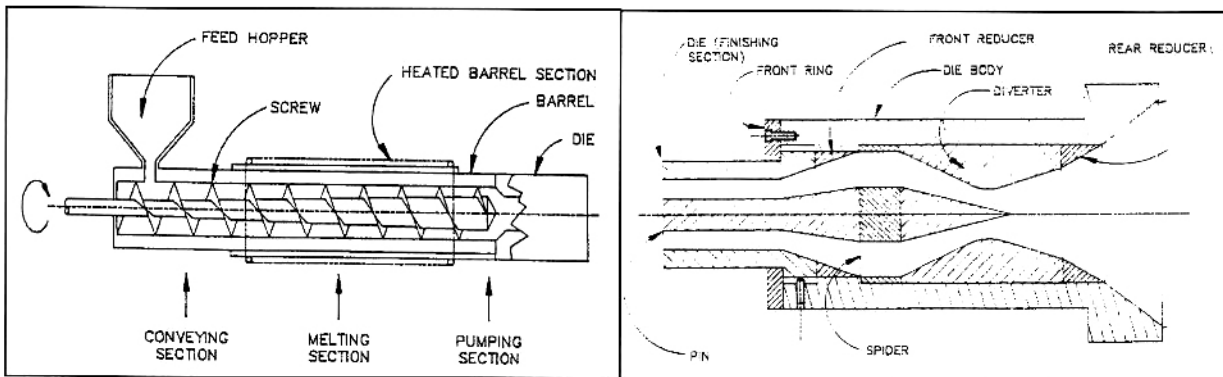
a) Esquema de la máquina utilizada en la extrusión de cerámicos. b) Ejemplo de la boquilla de una máquina de extrusión.
